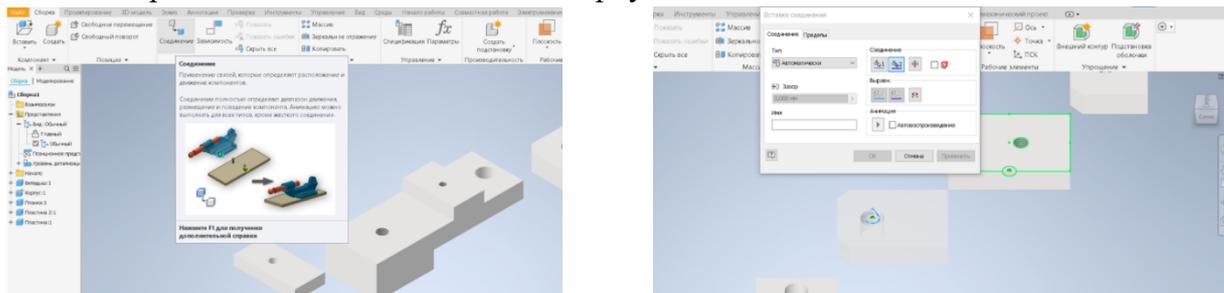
Команда «Соединение» и установка направления взгляда
